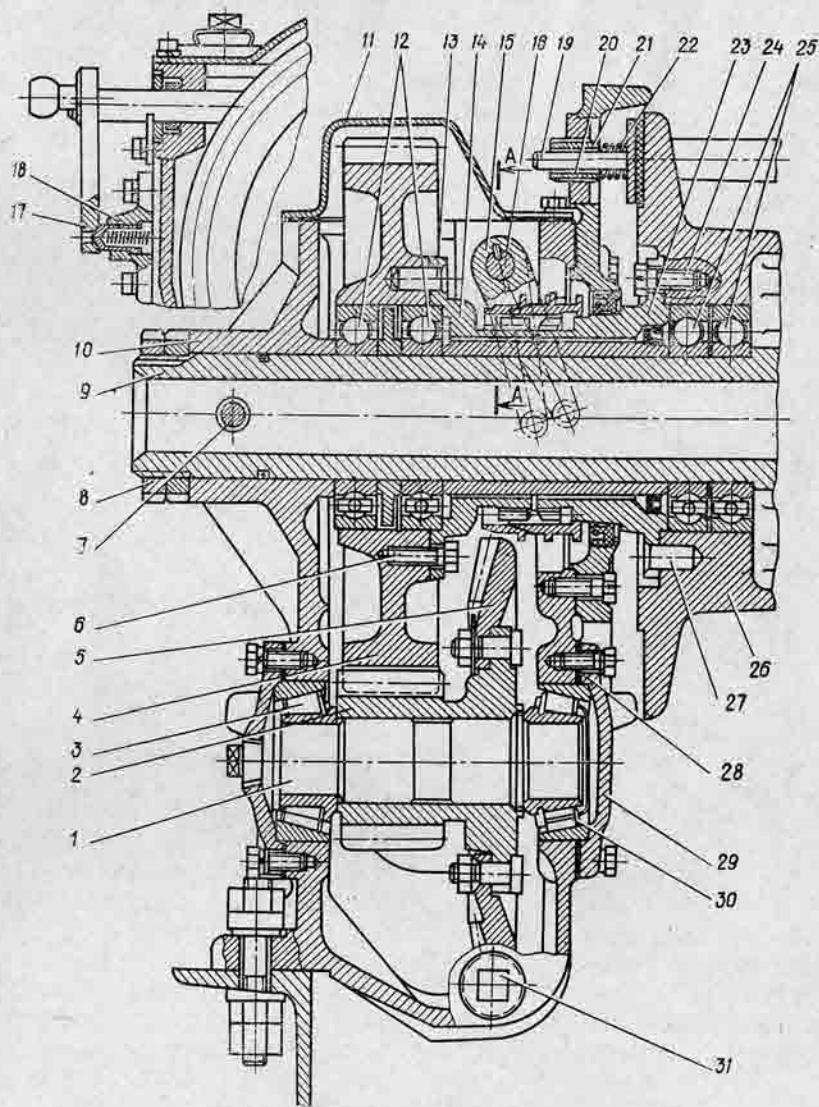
Коническо-цилиндрический редуктор лебедки;
